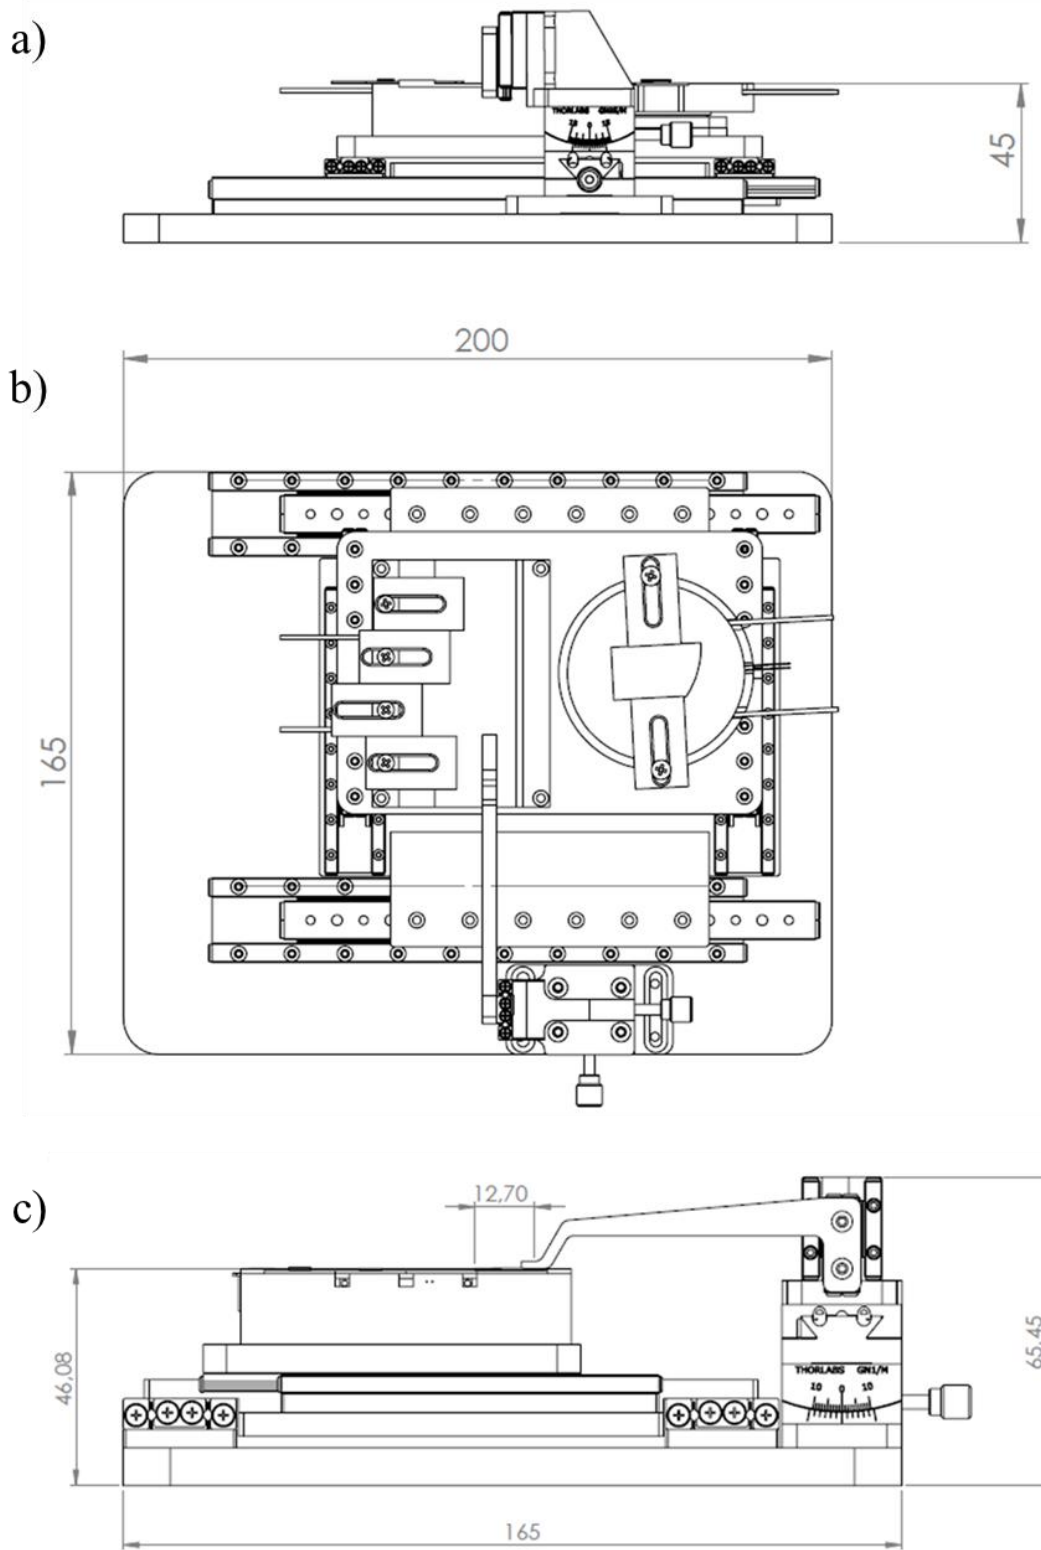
Dessin technique réalisé par Christophe Boyaval (a) vue de derrière (b) vue de dessus (c) vue de droite
